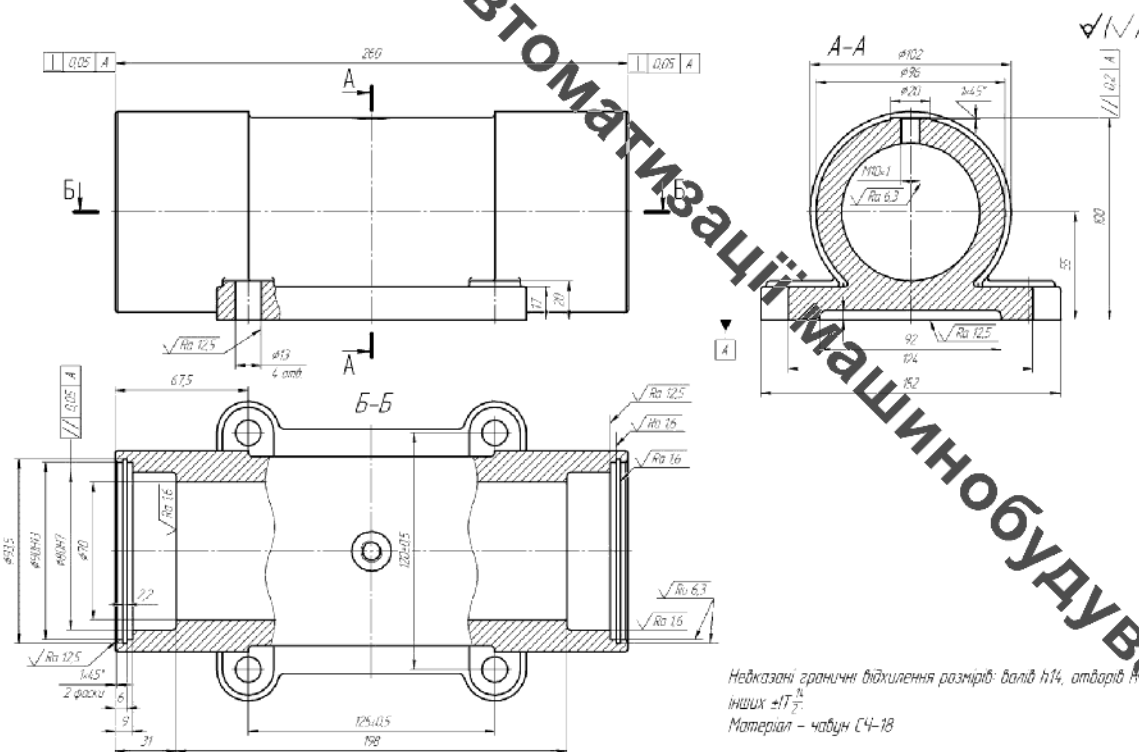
Ескіз маршруту механічної обробки деталі "Корпус"
